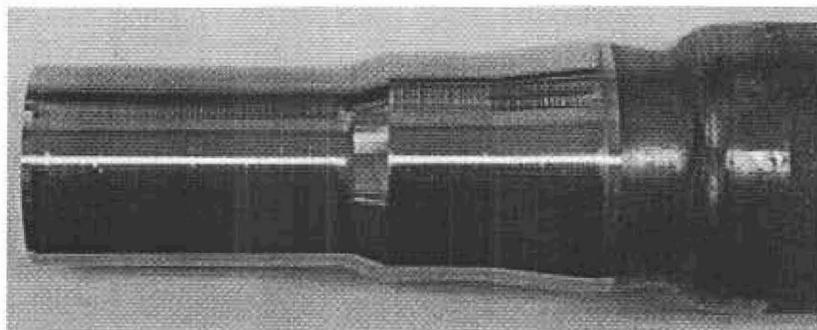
Beispiel eines hohles Umformteiles aus TRIP Stahl C-Mn-Si-Nb nach einem Drückwalzen mit 12% Walzabnahme
